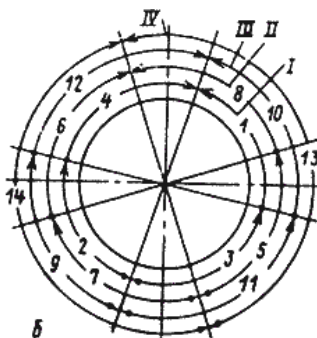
Порядок наложения слоев при сварке вертикальных неповоротных стыков труб:
